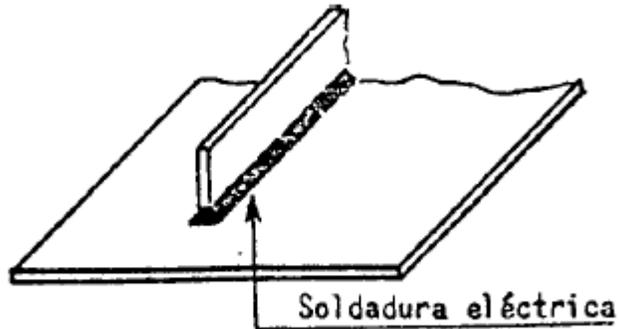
Chapas unidas por soldadura eléctrica: es necesaria la limpieza del cordón de soldadura
